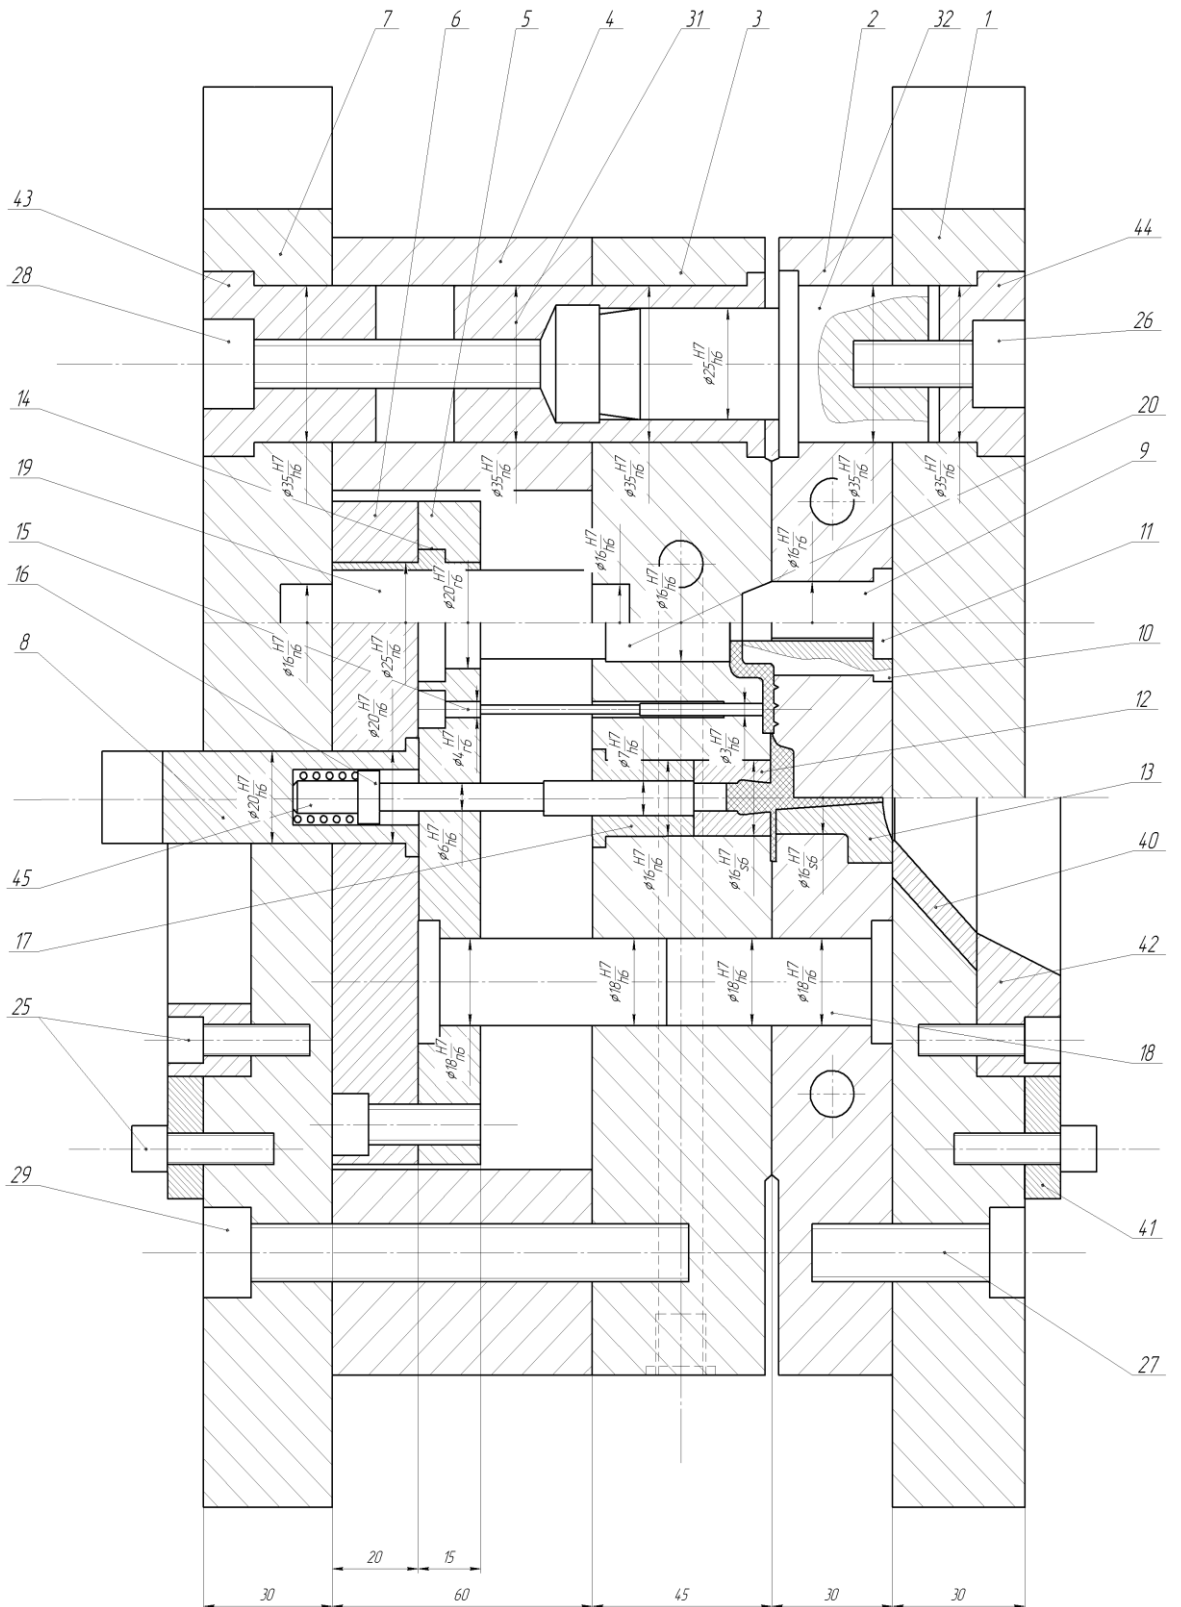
Конструкция пресс-формы для изготовления изделия «Крепление обивки двери передней» (разрез А-А)
